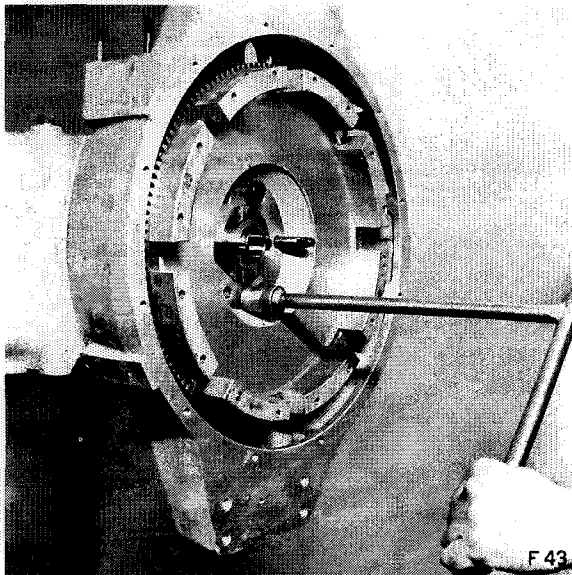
Lösen der Befestigungsschrauben am Motorschwungrad
